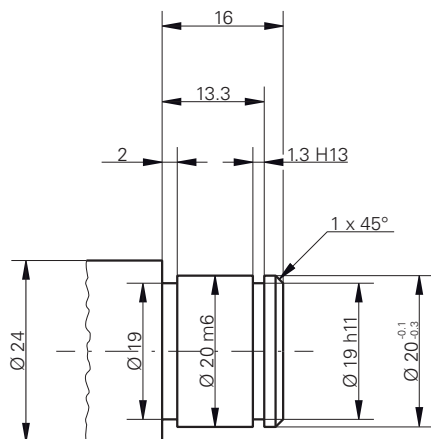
Peça de trabalho de exemplo – Desenho Técnico
